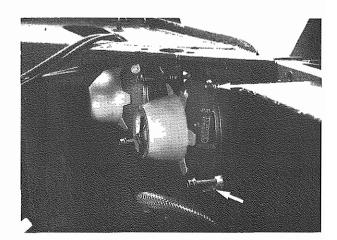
Viti di fissaggio proiettori Headlight screws
